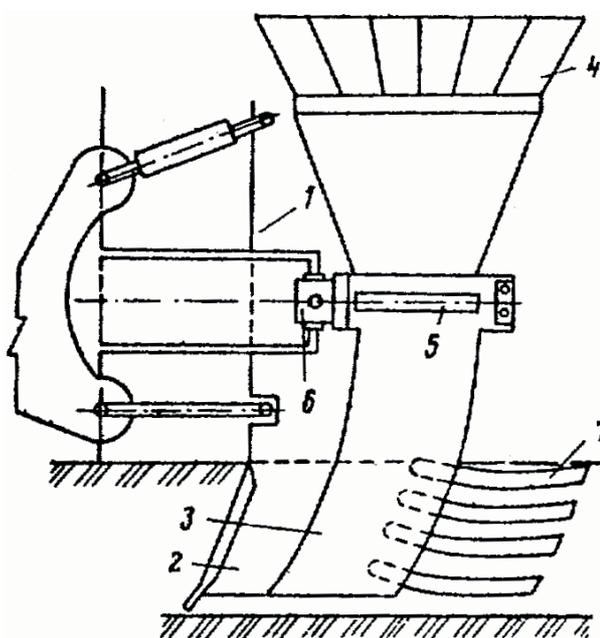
Однооперационный агрегат, подающий наполнитель из бункера в щель роторами: 1 – рама; 2 – щелерез; 3 – боковины щелереза; 4 – бункер; 5 – роторы; 6 – гидродвигатель; 7 – распределяющие прутки
